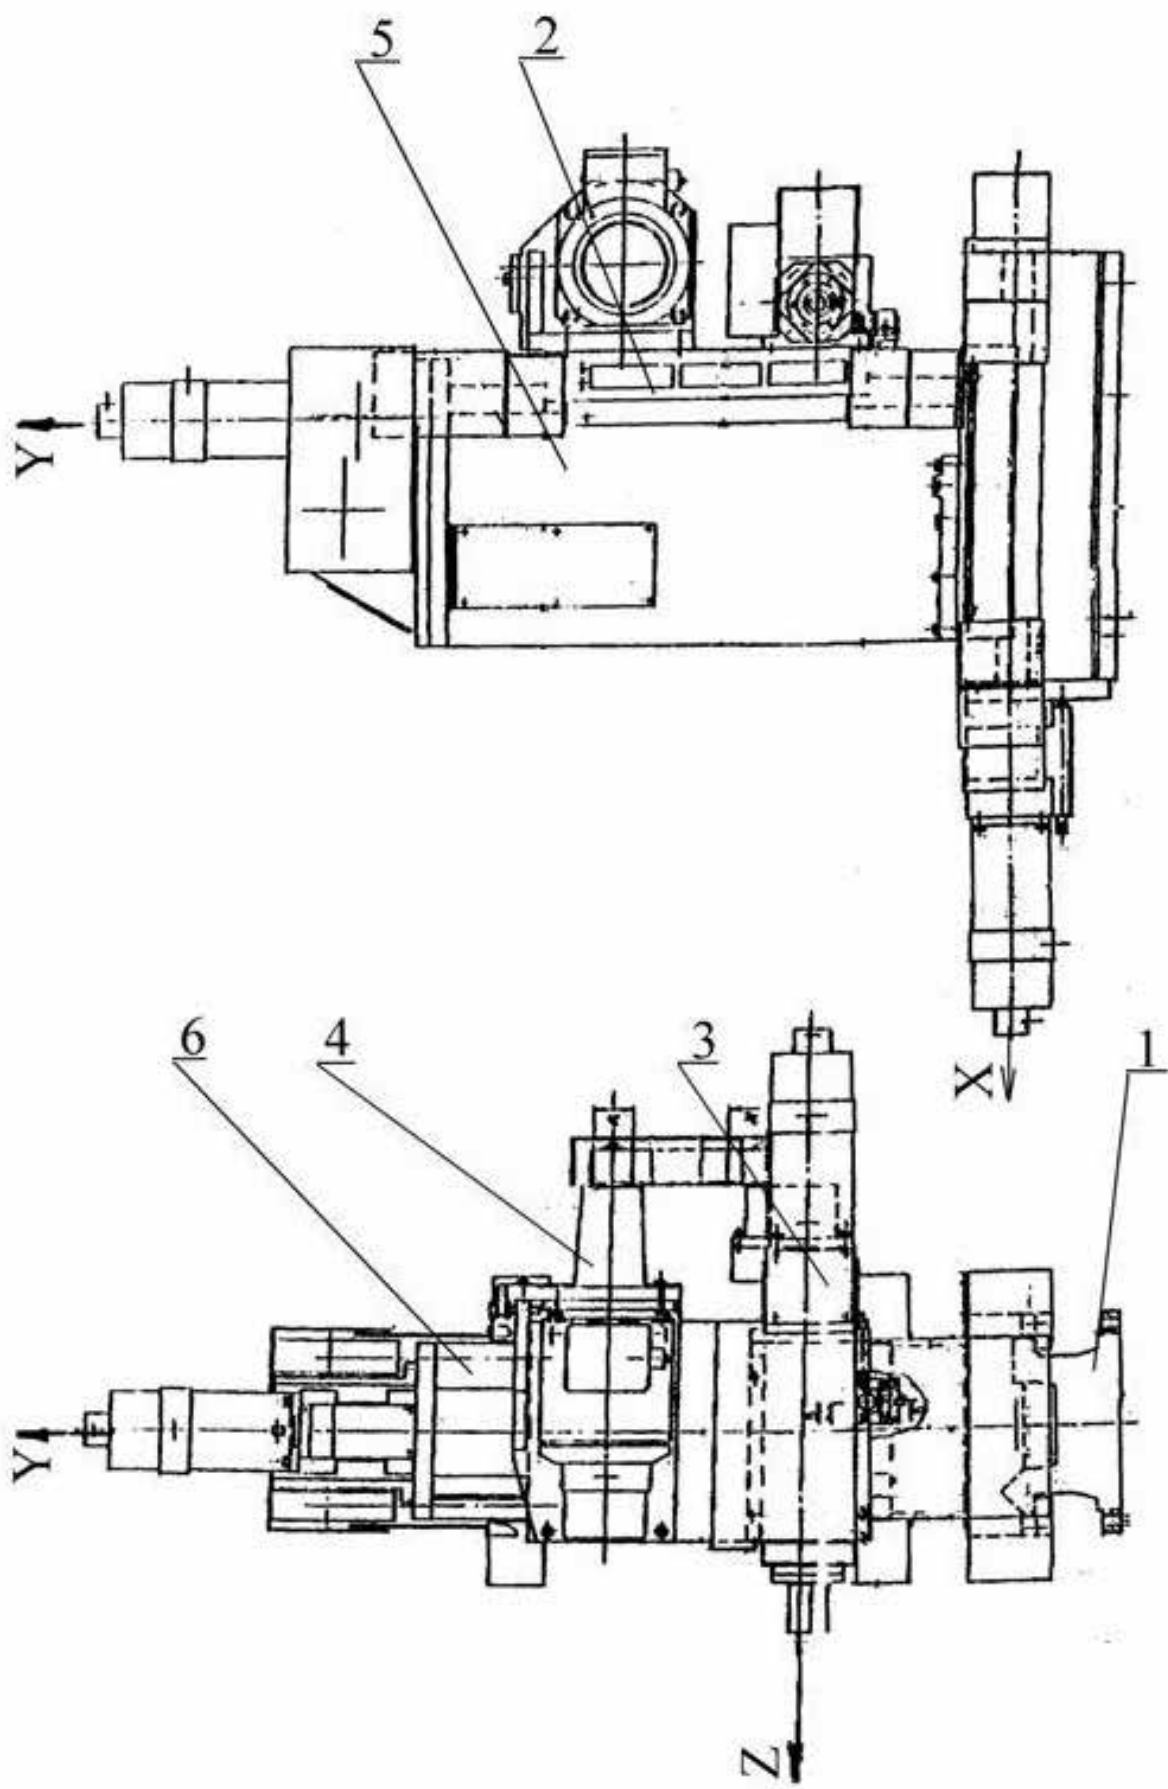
Трискоординатный силовой вузол STM 100
